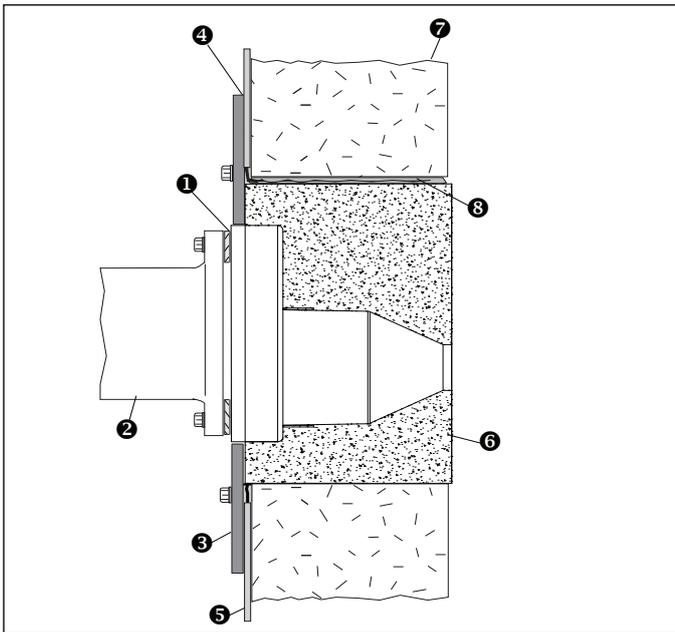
Solide, mit hitzebeständigem Material beschichtete Brennöfen
